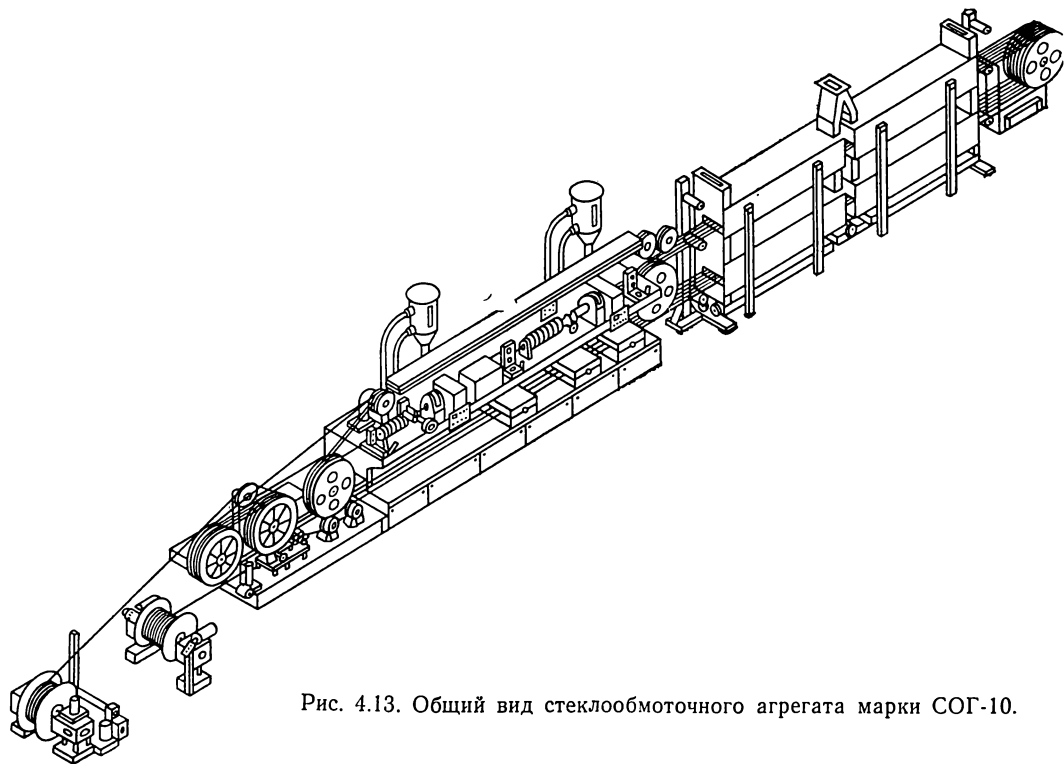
Общий вид стеклообмоточного агрегата марки СОГ-10.
